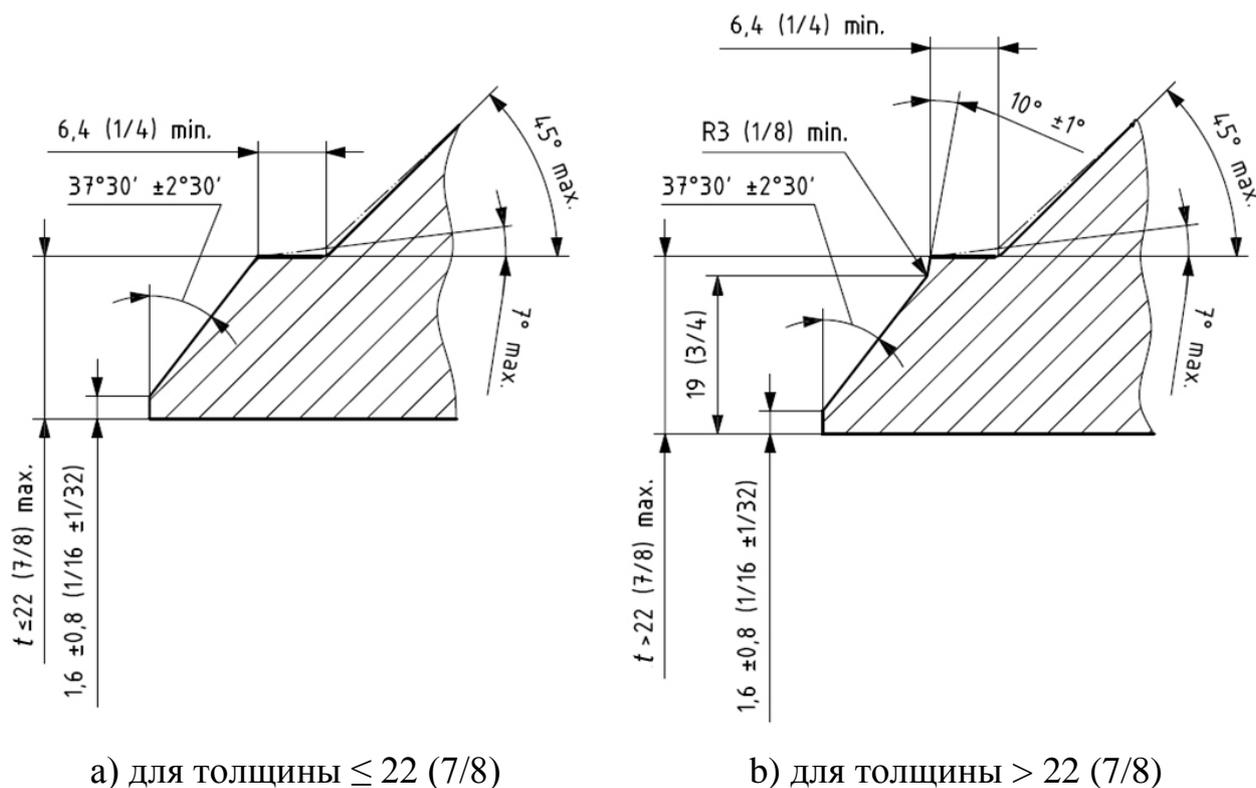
Разделка приварного конца для фланцев с приварными шейками типа 17SS и 17SV
